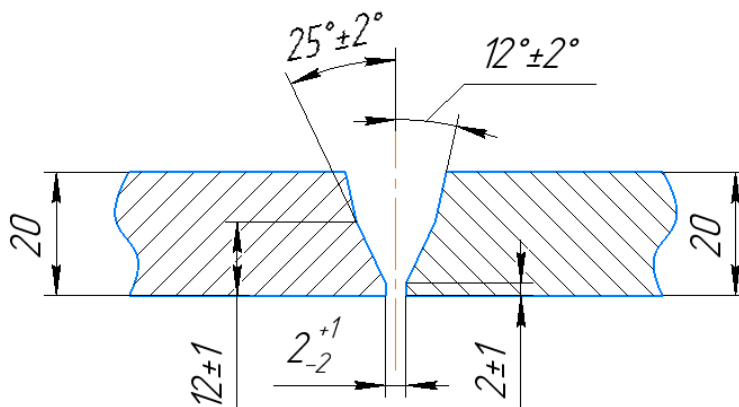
Размеры подготовленных кромок сварных элементов, тип сварного соединения С24 по ГОСТ 5264-80
